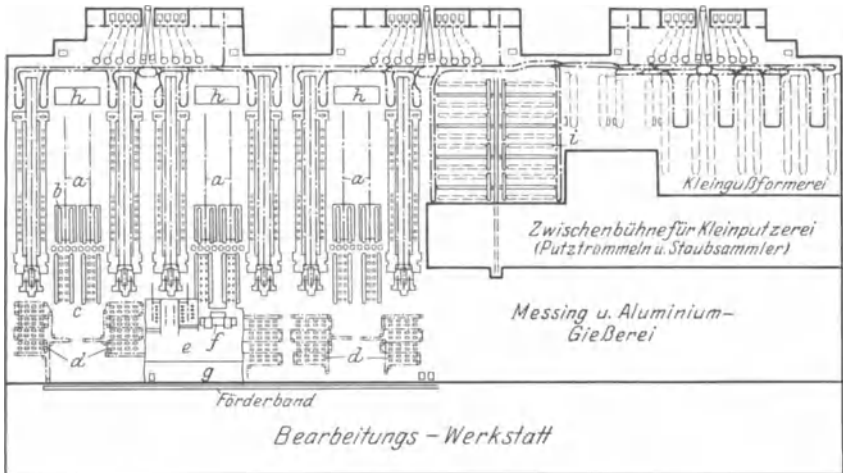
Grundriß der Ford-Gießerei in River-Rouge.
